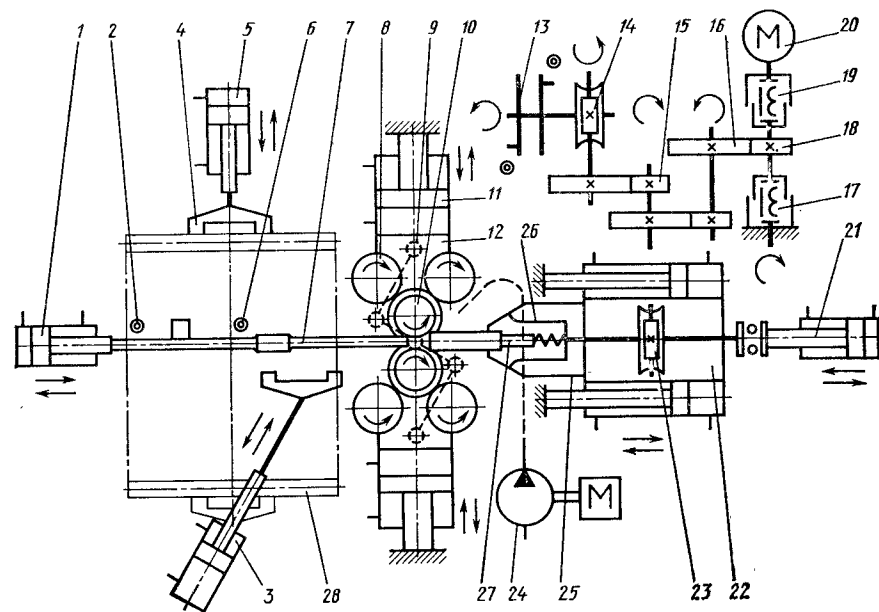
Кинематическая схема автомата мод. Л345.61.111 для продольной раскатки заготовки шпильки:
